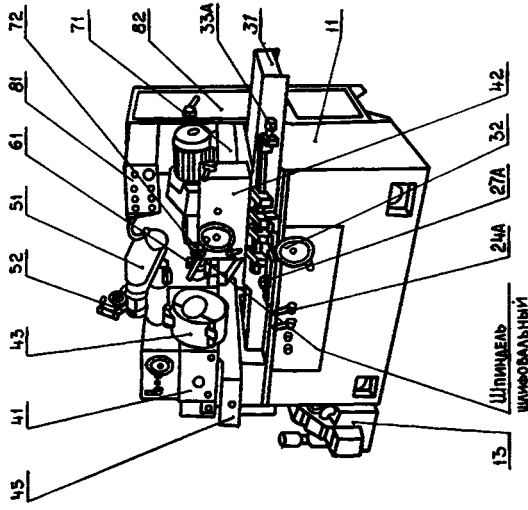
Общий вид станка модели 3К227А с обозначением узлов
